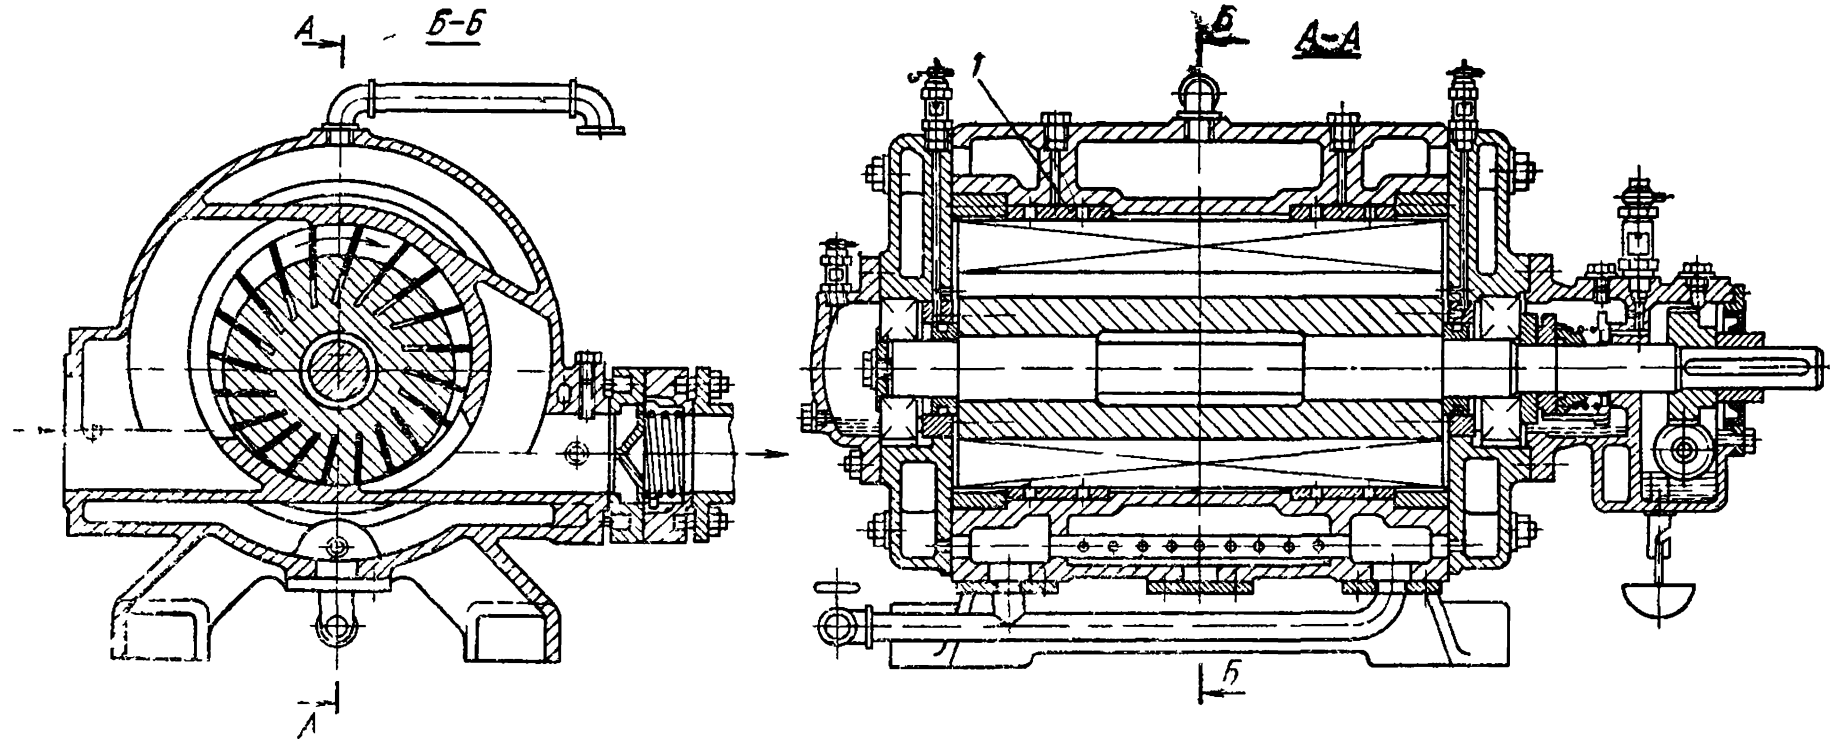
Пластинчатый компрессор с наклонными лопатками и разгрузочными кольцами фирмы Клейн, Шанцлин и Беккер (ФРГ)
